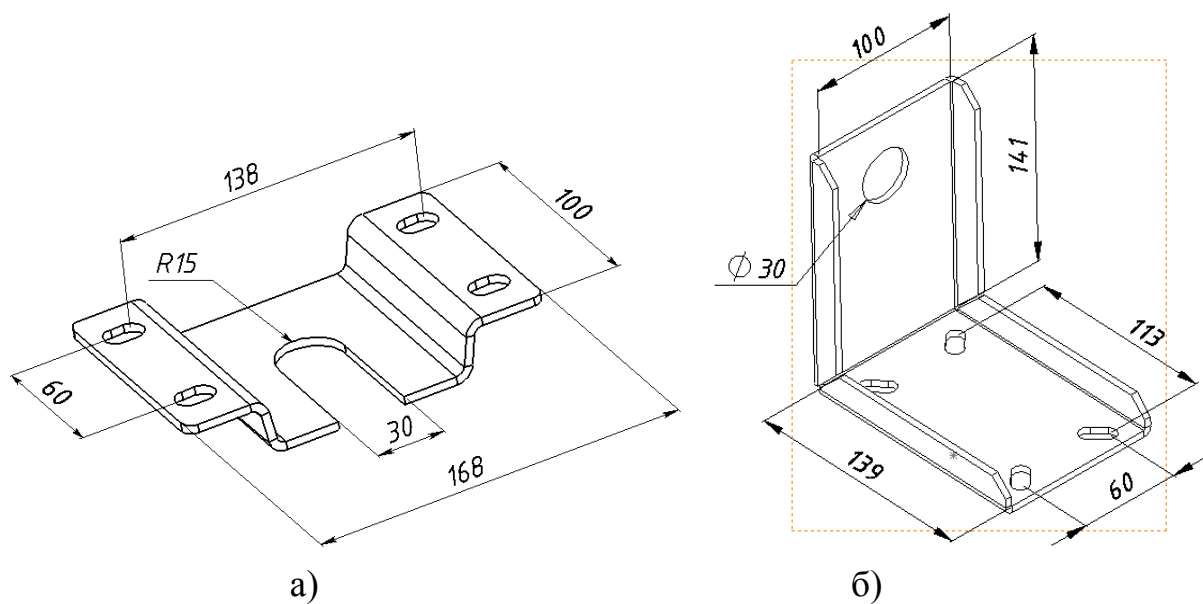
Общий вид и присоединительные размеры креплений модуля «ИМПУЛЬС-2-Т»
